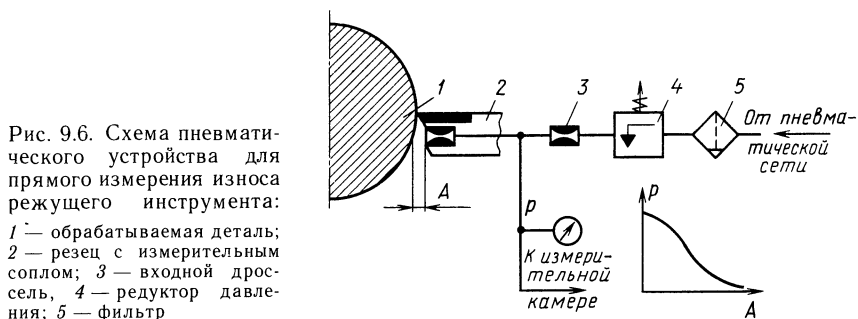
Схема пневматического устройства для прямого измерения износа режущего инструмента:
